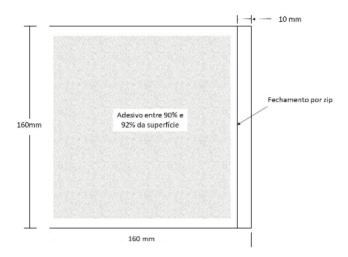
Envelope plástico para embalagem da urna eletrônica
